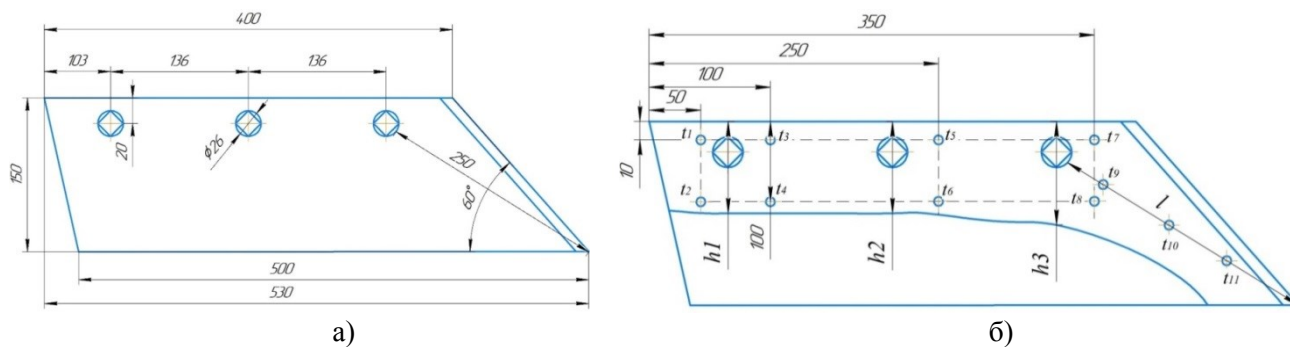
Изучаемая деталь (а - чертеж ; б – схема измерения ножа)
